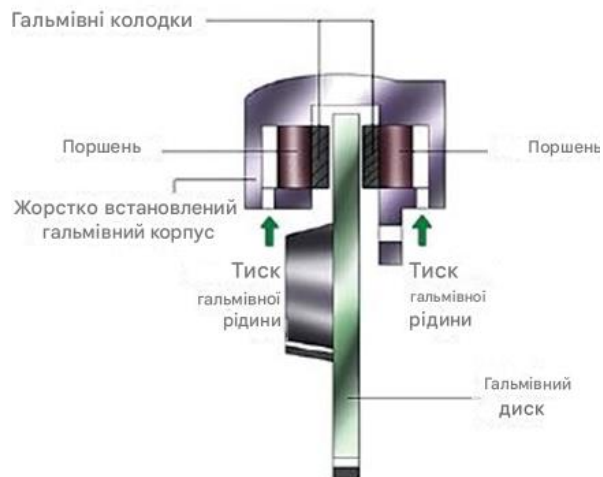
Робота дискового гальмівного механізму з жорстко встановленим корпусом гальма [2]
